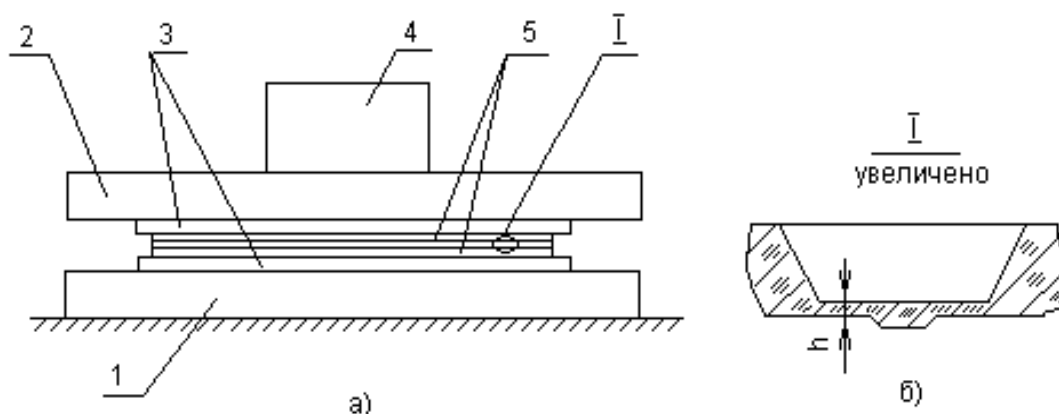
Приспособление для группового соединения микромеханических деталей:
